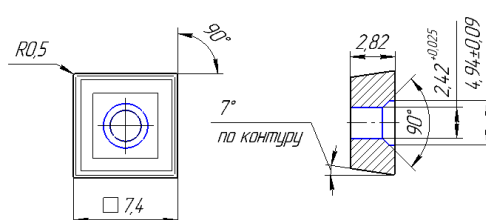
Пластина для сверления – 880-0403W0,5H-P-GR
